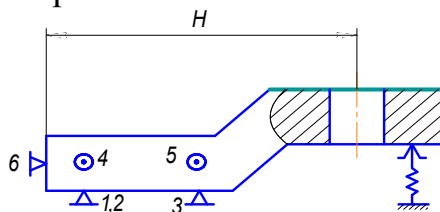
Пример установки заготовки на основные и вспомогательные опоры
